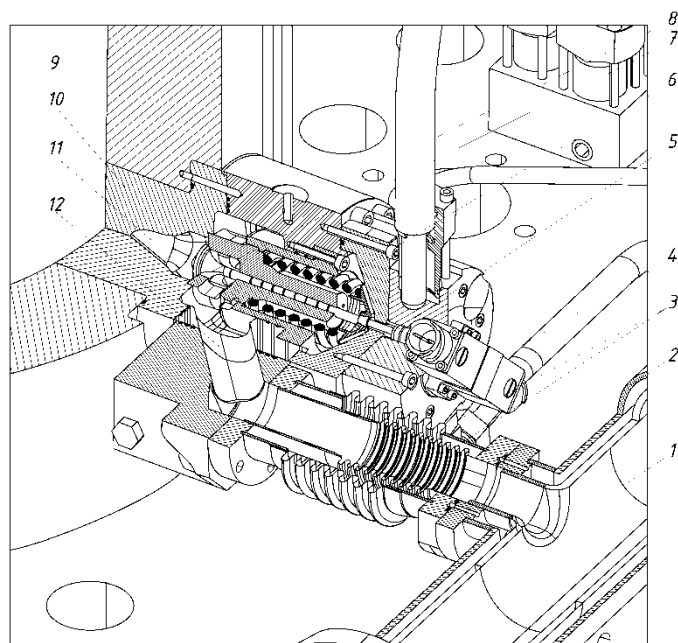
Установка газового клапана на втулке цилиндра двигателя RT-flex50DF: 1 – газовая магистраль; 2 – внешняя оболочка газовой магистрали; 3 – внешний и внутренний сильфон; 4 – электромагнитный клапан управления; 5 – гидравлический поршень привода клапана; 6 – пружина закрытия клапана; 7 – газовый клапан; 8 – гидравлическая магистраль привода клапана; 9 – втулка цилиндра; 10 – корпус газового клапана; 11 – канал подвода ГТ в рабочий цилиндр; 12 – канал подвода ГТ к газовому клапану
